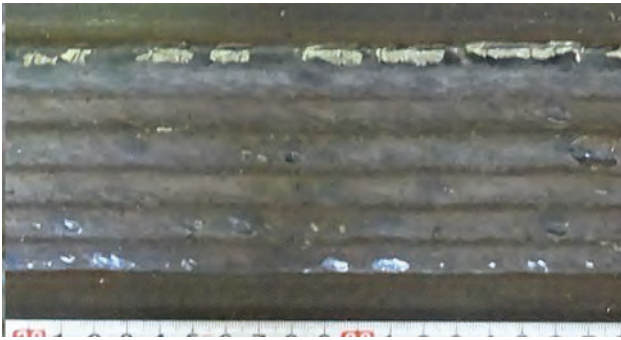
SX-80CF 下向溶接 (板厚 80mm)の
